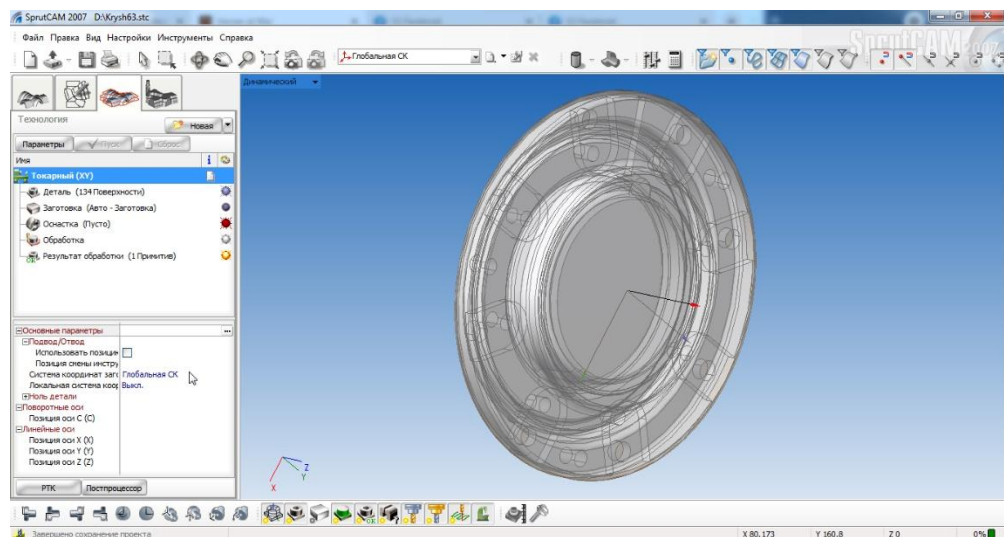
Деталь та заготовка в системі СПРУТ-САМ
